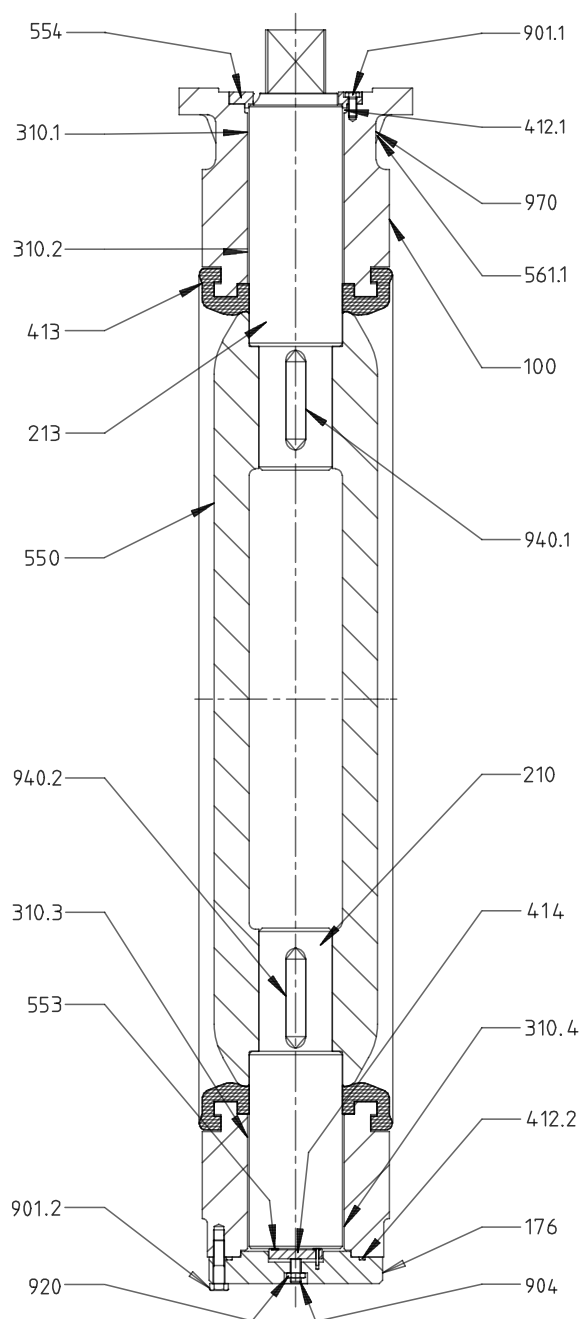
Vista de sección de MAMMOUTH para DN 1050 - 1200
